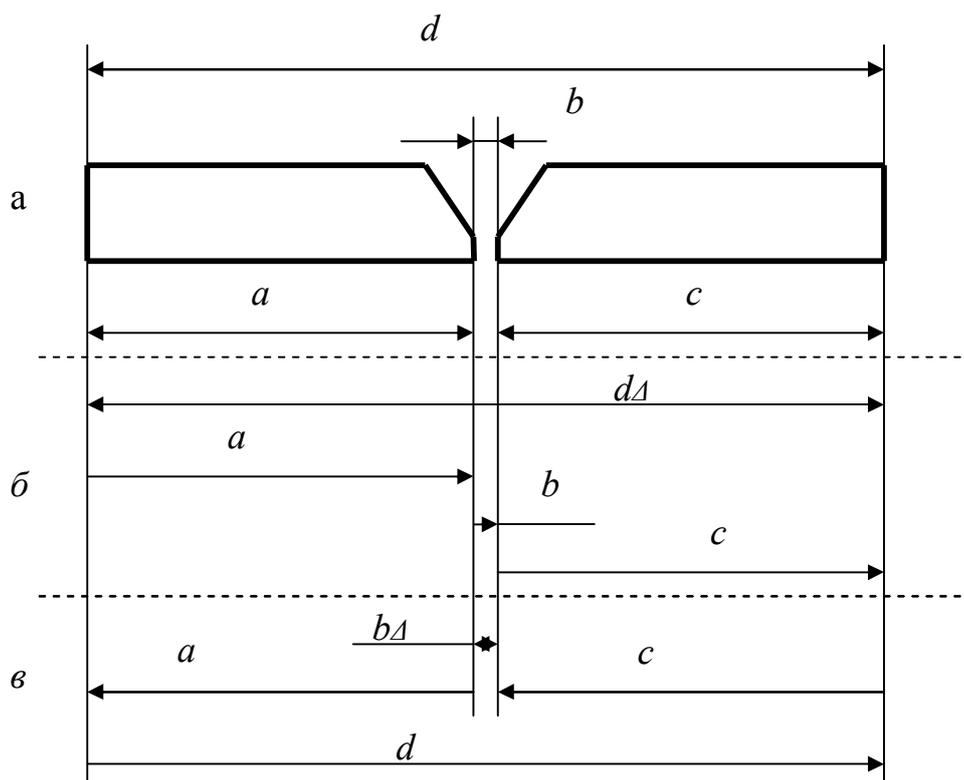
Сборочная размерная цепь с зазором-компенсатором
